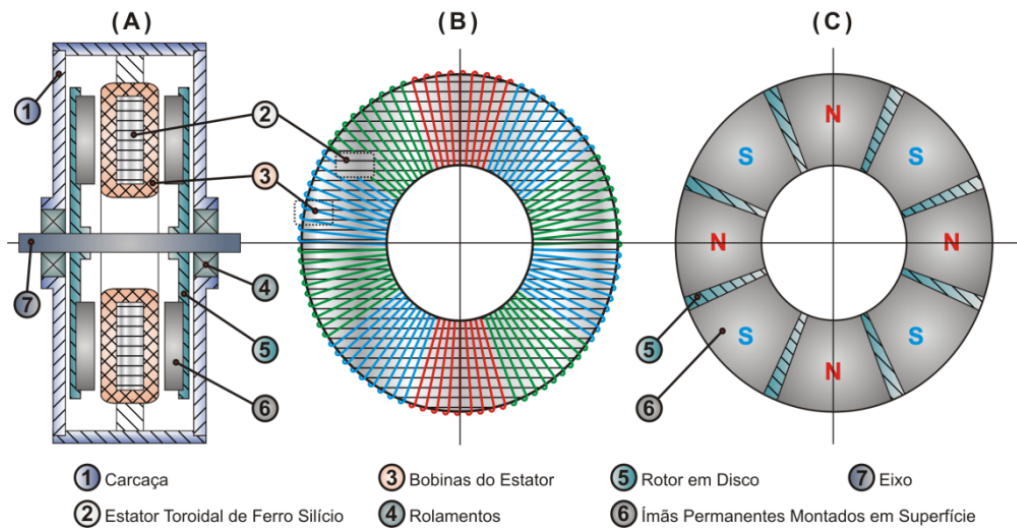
Máquina de fluxo axial do tipo toroidal (“*Torus Machine*”). (A) Estrutura construtiva, (B) vista frontal do estator bobinado, (C) vista frontal do disco de ímãs.
